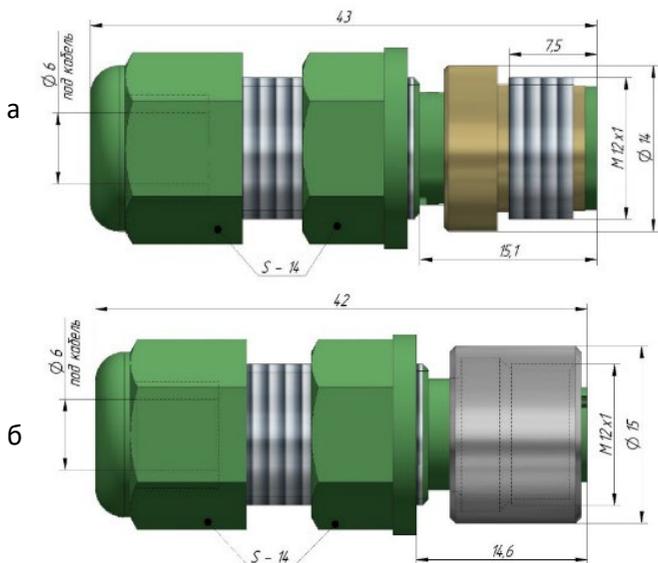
Внешний вид и габаритные размеры разборных кабельных разъемов:
